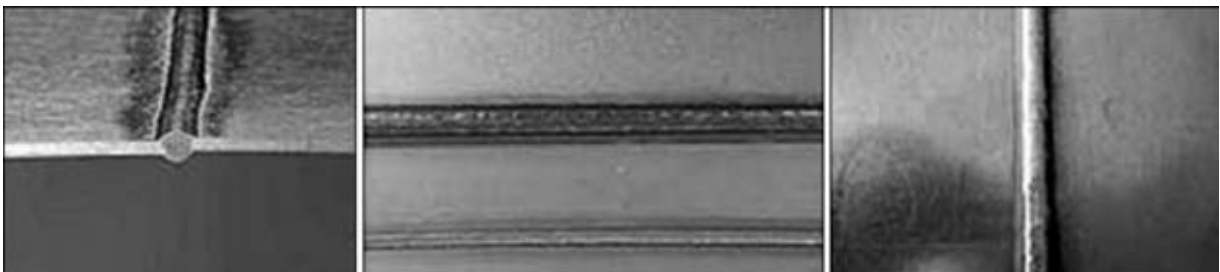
Внешний вид сварных швов при использовании СМТ процесса
